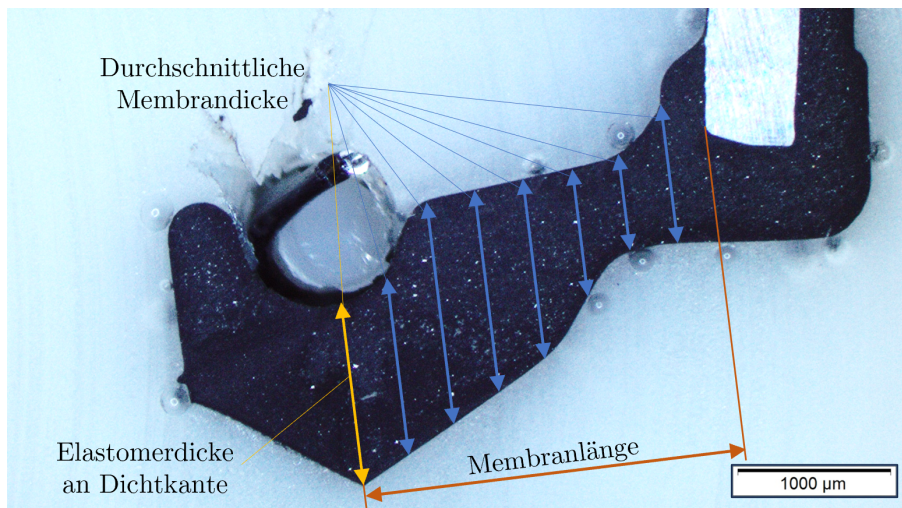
Schnittbild der Membran und Dichtkante des in Harz eingegossenen unmontierten RWDR mit Feder, die Membranlänge (orange, 2,53 mm), die Elastomerdicke an der Dichtkante (gelb, 1,22 mm), sowie die durchschnittliche Membrandicke (blau, gelb, 1,11 mm) sind gekennzeichnet
